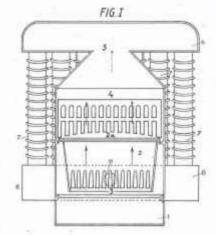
Fig. I. — COUPE LATÉRALE DE L'ENSEMBLE DU DISPOSITIF BREVETÉ
